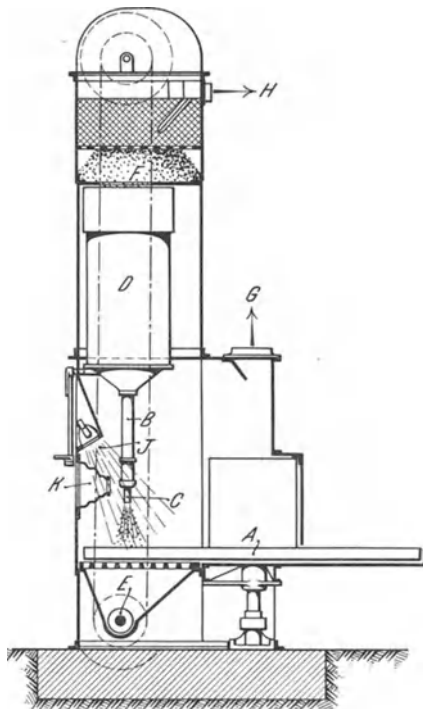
Blasgehäuse mit pendelnd aufgehängter Sandstrahldüse.
